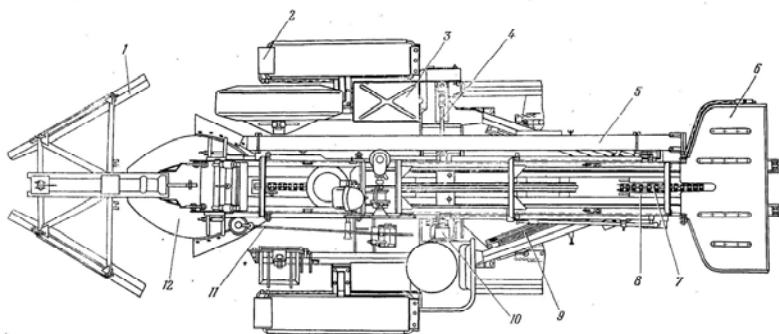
Минный заградитель ПМЗ-4 в рабочем положении (вид сверху): 1 – обратный отвал; 2 – задний фонарь; 3 – ящик для ЗИП; 4 – приводной вал трансмиссии; 5 – направляющая труба (в транспортном положении); 6 – приемный лоток; 7 – цепной транспортер; 8 – механизм противозаклинивания; 9 – запасные ножи плуга; 10 – фрикцион; 11 – предохранительный трос; 12 – плуг с прижимами
